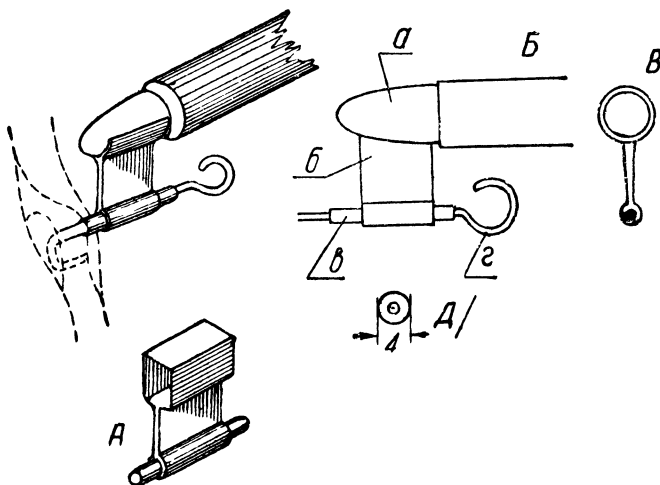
Подшипник: А — конструкция подшипника при рейке прямоугольного сечения; Б и В — конструкция подшипника при камышевой рейке
